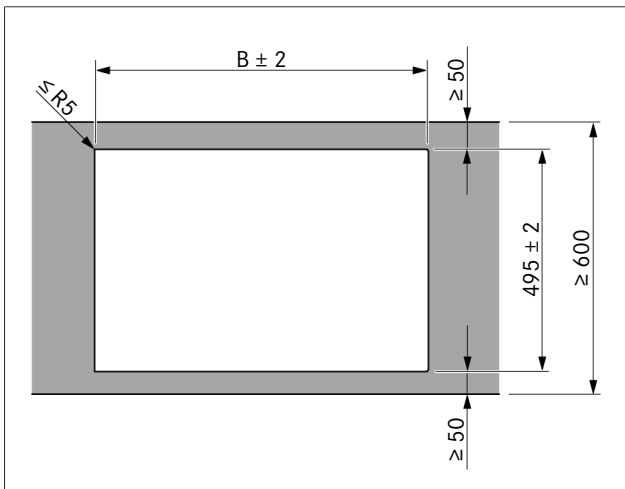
Medidas de recorte para montagem por sobreposição
